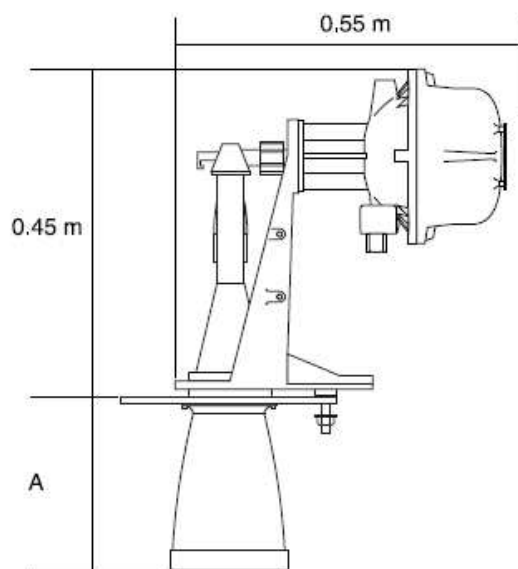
6: Dimensiones del Medidor de Tubo Guía.
